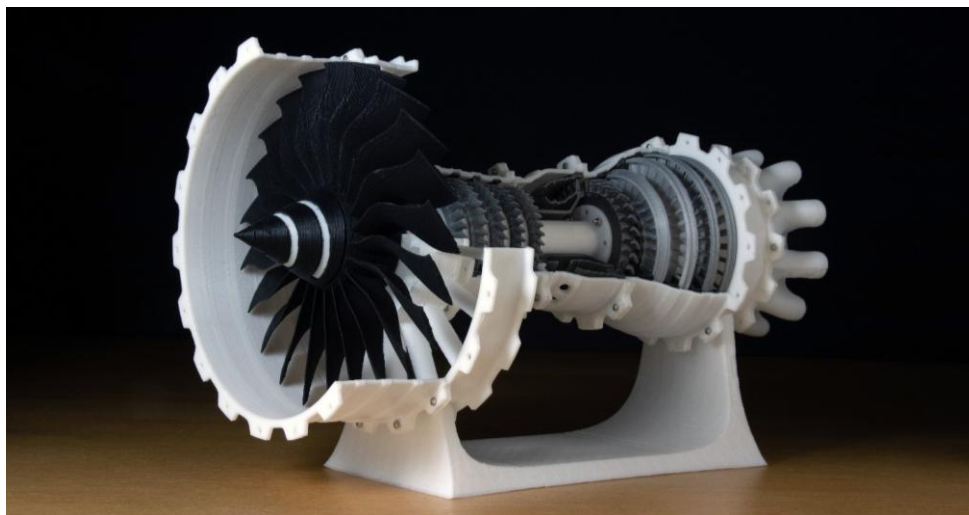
Pieza aeronáutica fabricada mediante impresión 3D [21]
